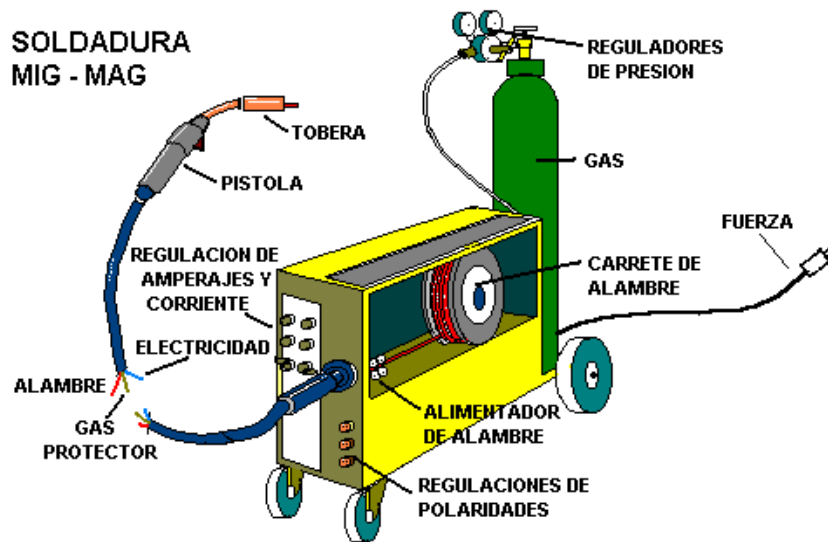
Equipo de la soldadura GMAW. [37]
